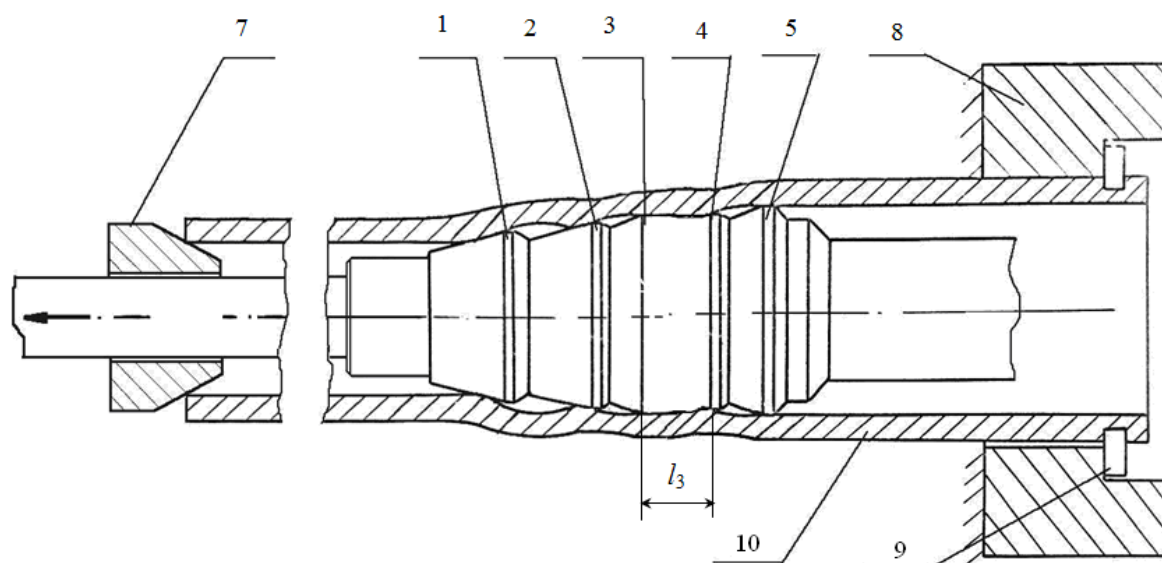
Деформування заготовки за схемою розтягнення з поліпшеним базуванням
